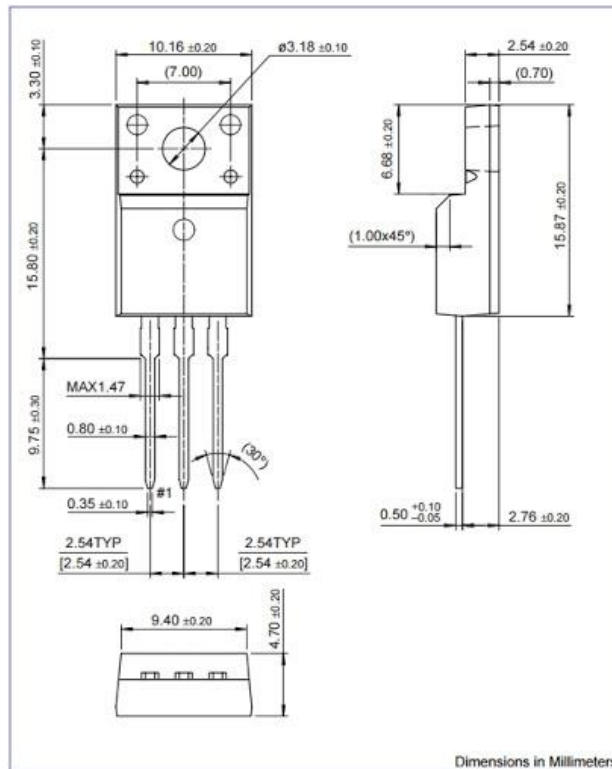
Габаритні розміри мікросхеми KIA7805API-U / PF
